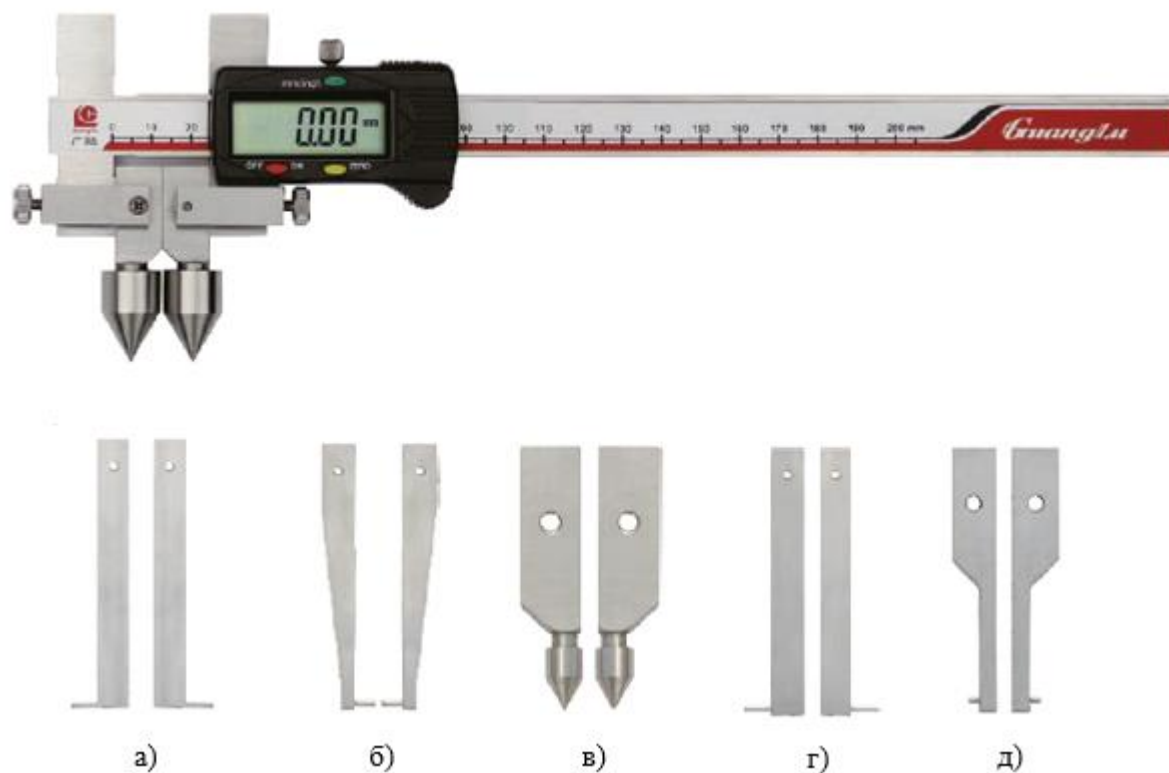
Общий вид штангенциркулей модификации 118, исполнений 412, 413 и комплекты сменных измерительных губок; а) – с плоскими измерительными поверхностями; б) г), д) – цилиндрические с точечными измерительными поверхностями; в) – цилиндрические с коническими измерительными поверхностями для определения расстояния между центрами отверстий
